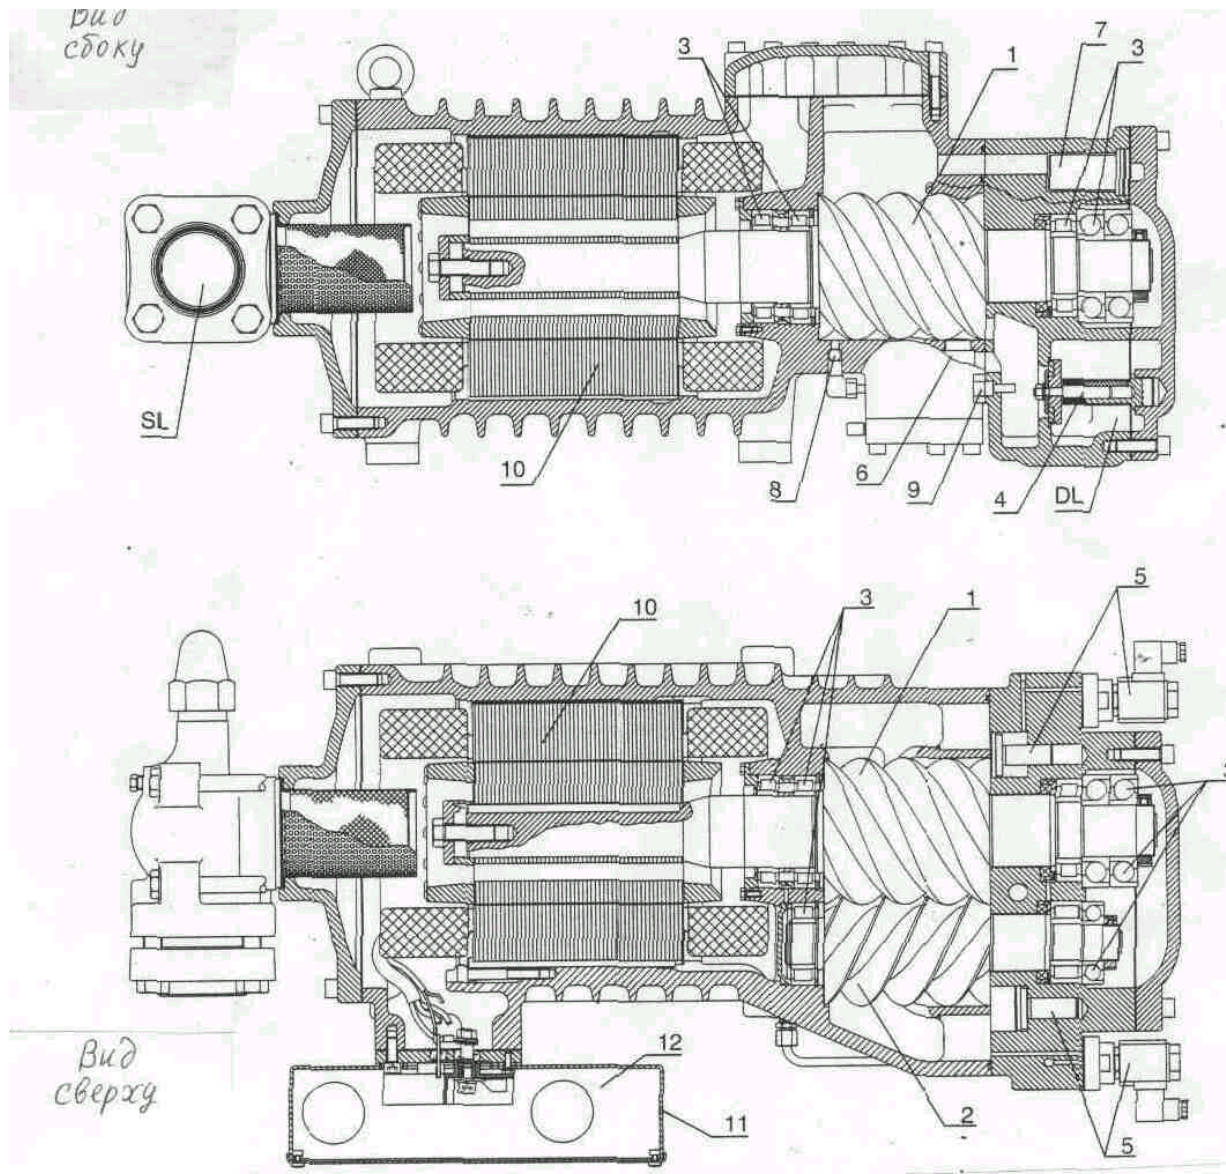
1 1. Схема герметичного винтового компрессора HS. 74
